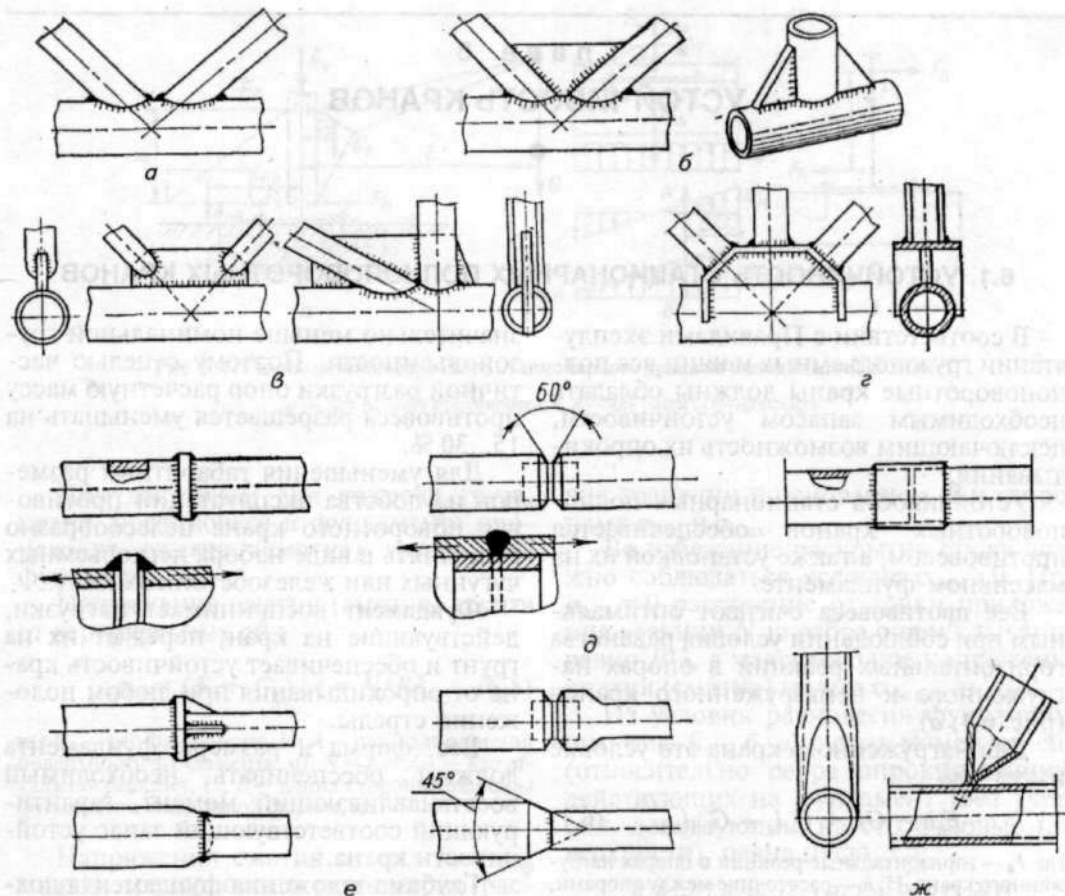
Примеры стыковки трубчатых профилей в узлах металлоконструкций:
